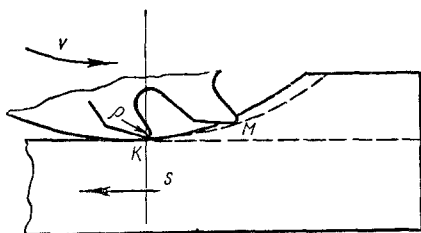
Схема врезания зуба при цилиндрическом фрезеровании против подачи
